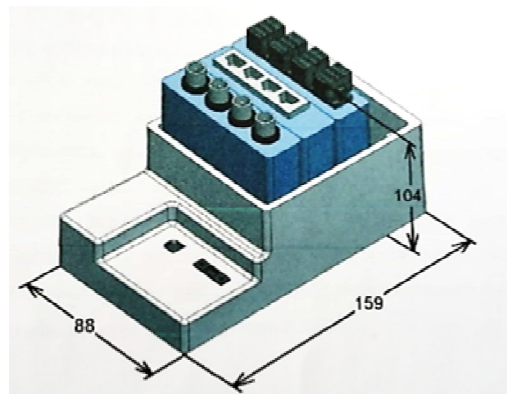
Внешний вид и габаритные размеры интерфейсного блока
